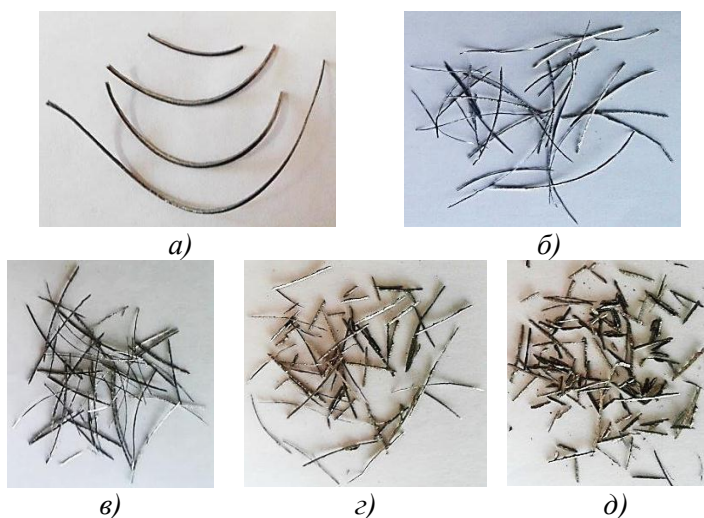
Стружки полученные при обработке отверстий инструментом, оснащенный чашечным резцом с наплавкой из материала STOODYM7-G
